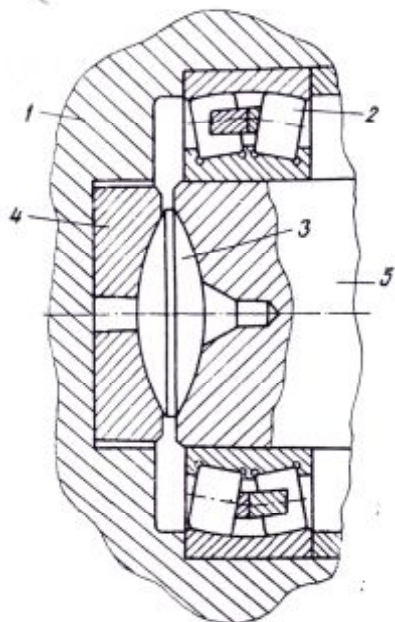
Конструкция опоры с шаровым упорным подшипником в виде линзы:
